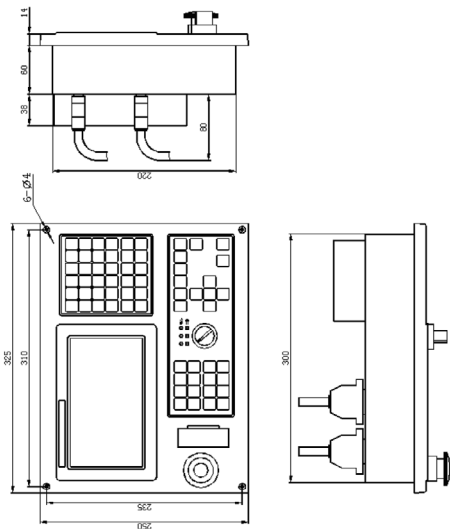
Габаритный чертеж контроллера RZNC-0305
